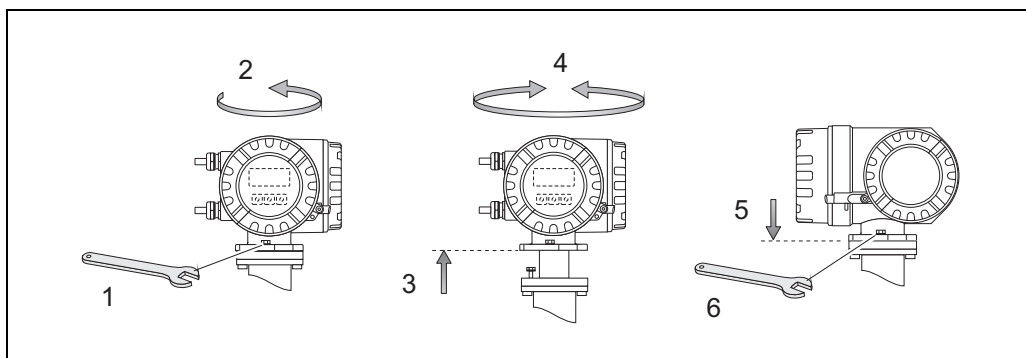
Поворот алюминиевого корпуса преобразователя, погружаемого в среду
